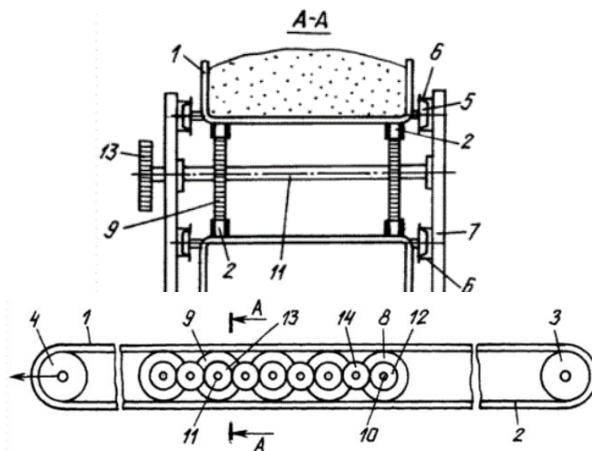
Пластинчатый конвейер: 1 – пластинчатая лента; 2 – тяговая цепь; 3 – приводная звездочка; 4 – натяжная звездочка; 5 – ходовые катки; 6 – направляющие; 7 – стойки; 8 – приводные звездочки; 9 – зубчатое колесо; 10,11 – вал; 12,13 – зубчатые колеса; 14 – промежуточные зубчатые колеса
